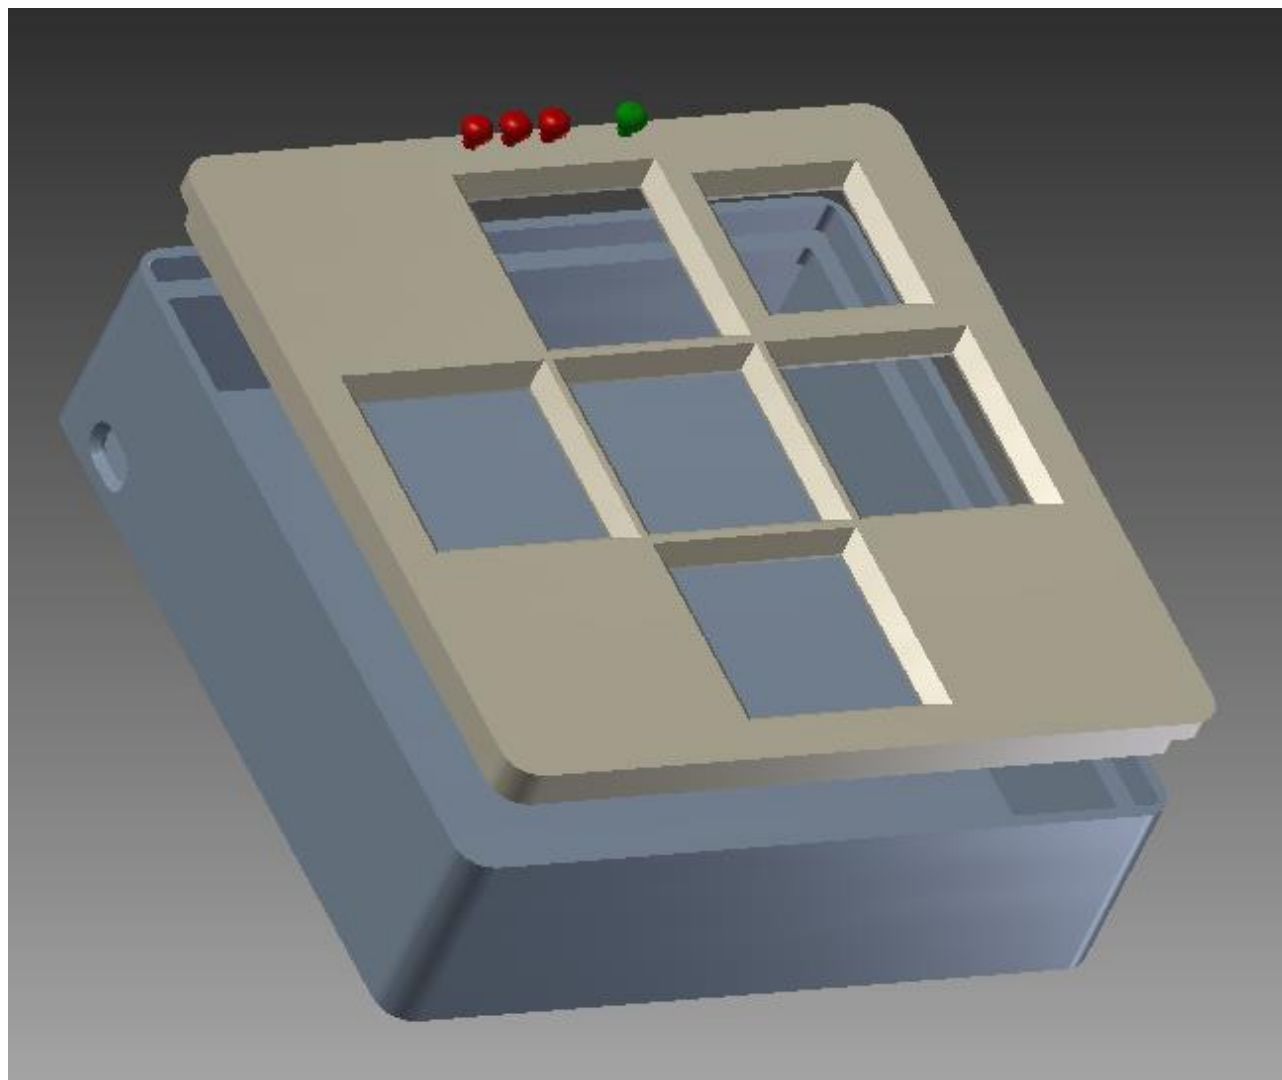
Modelo cubierta del teclado (vista ensamble)
